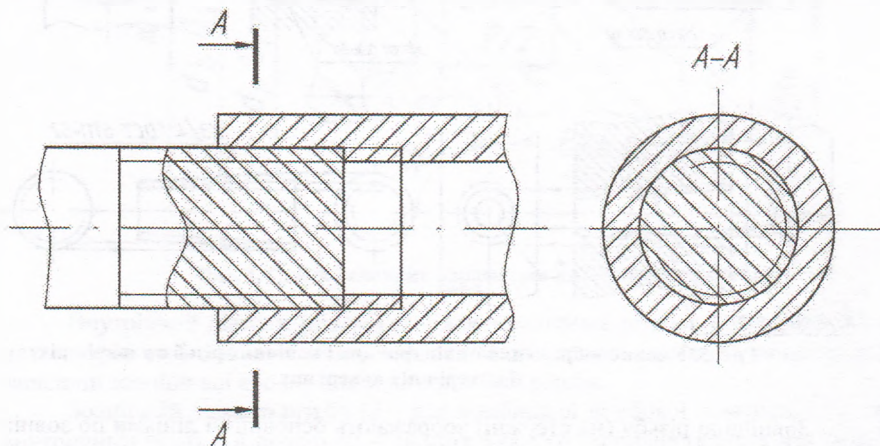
Умовне зображення різьбового з'єднання двох деталей
